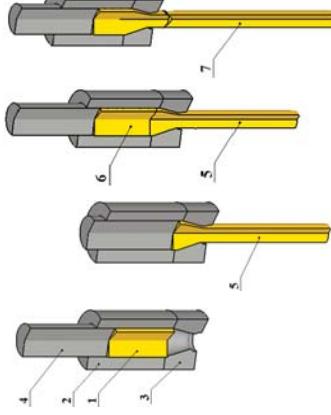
Розрахункові схеми в розрізі на початку та в кінці видавлювання першої та другої заготовки
